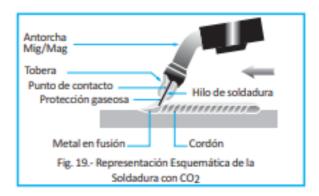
Representación esquemática de la soldadura con CO2 (Soldexa, 1981, p.31). Tomado de "Manual de soldadura"
